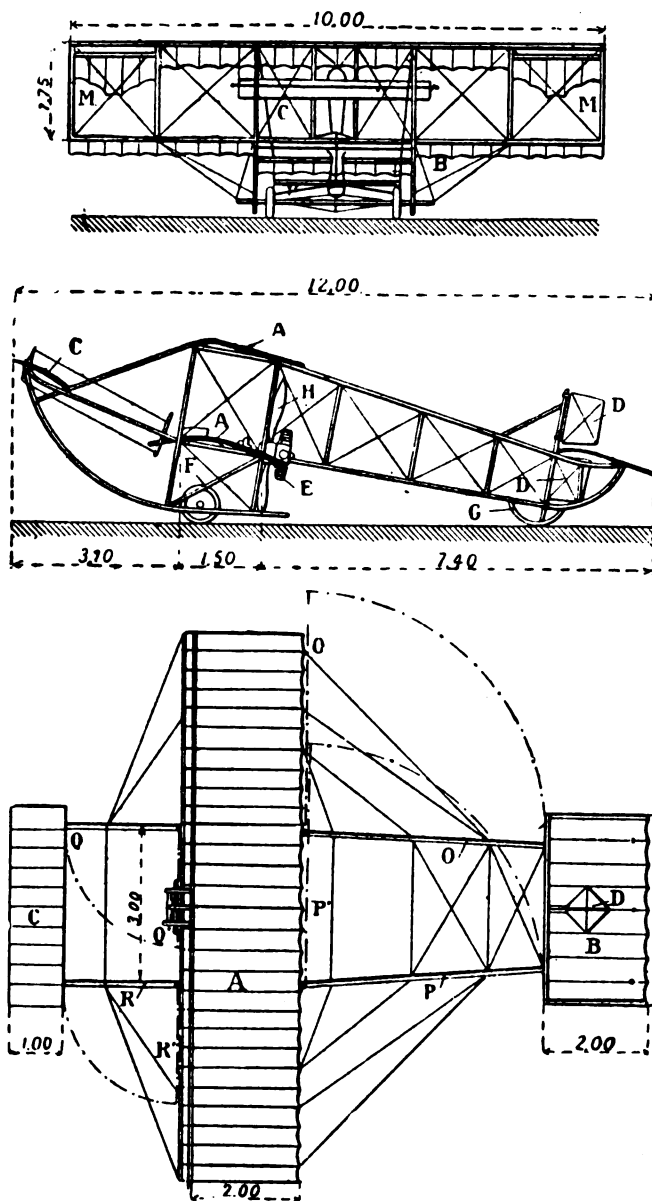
Biplano Sommer. - Vista, sezione e pianta.
